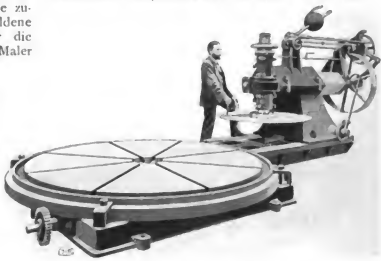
Kältsägemaschine von Gustav Wagner in Reutlingen.
